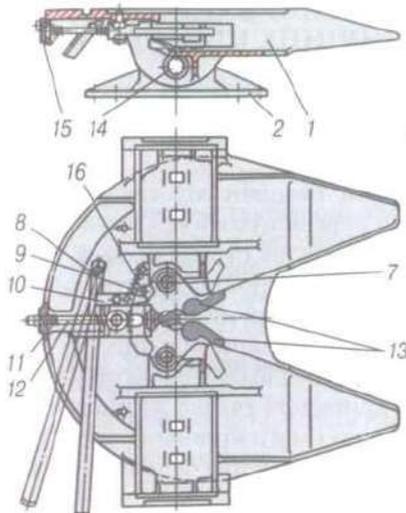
Сідельно-зчіпний пристрій:
